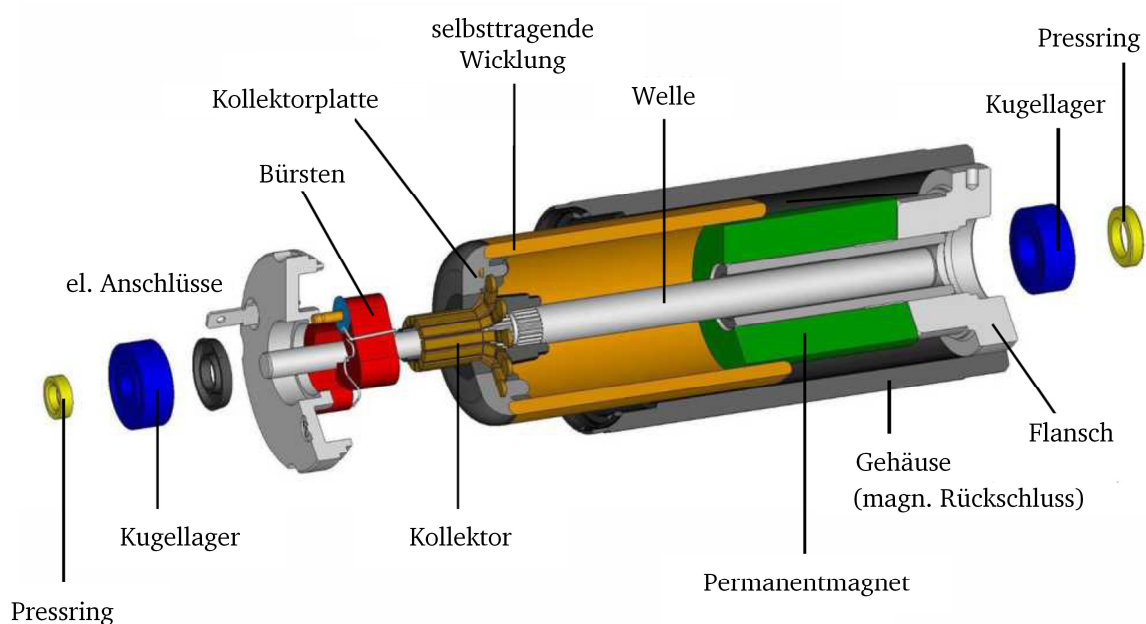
Aufbau eines mechanisch kommutierten Glockenläufermotors [68].
